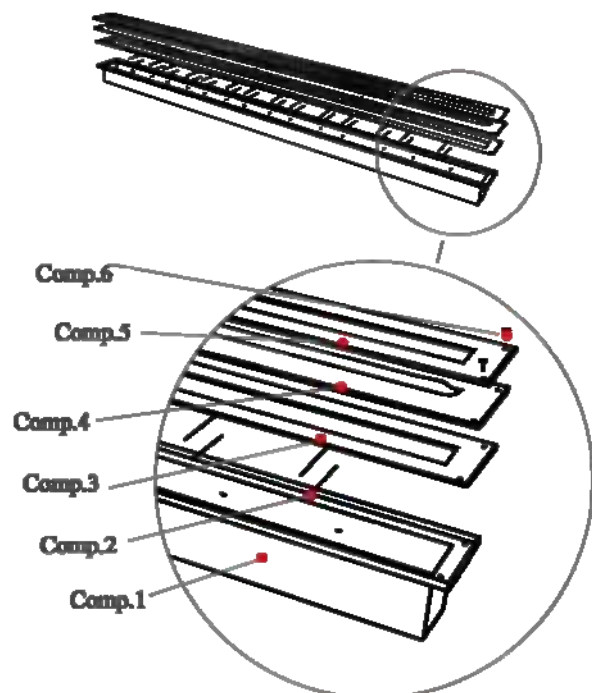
Perspectiva explodida da peça 1 e seus componentes.
